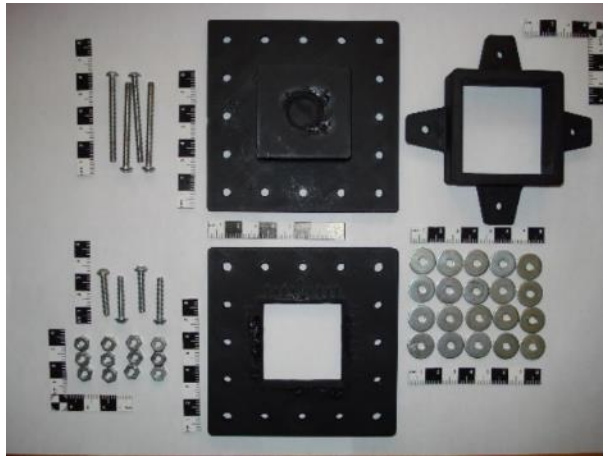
Total de piezas involucradas en el ensamble del receptor solar
